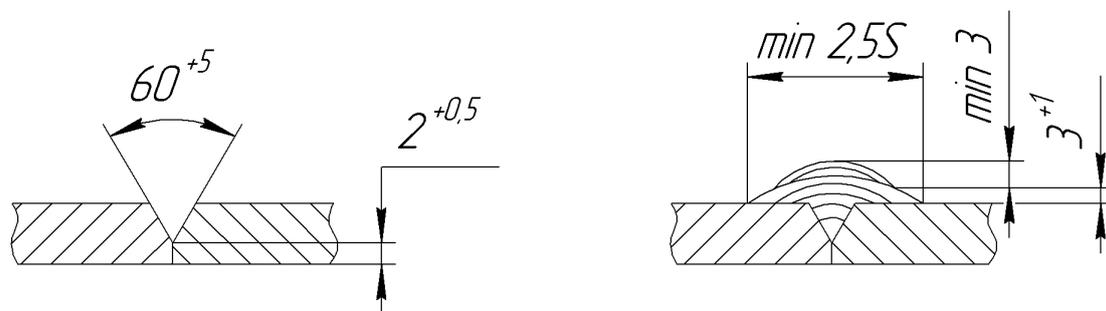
Геометрические параметры сварных соединений труб с силикатно-эмалевым покрытием с повышенным усилением.
